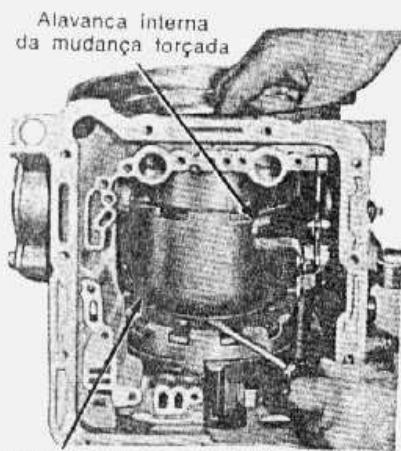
remoção do tambor impulsor e trem de engrenagens
